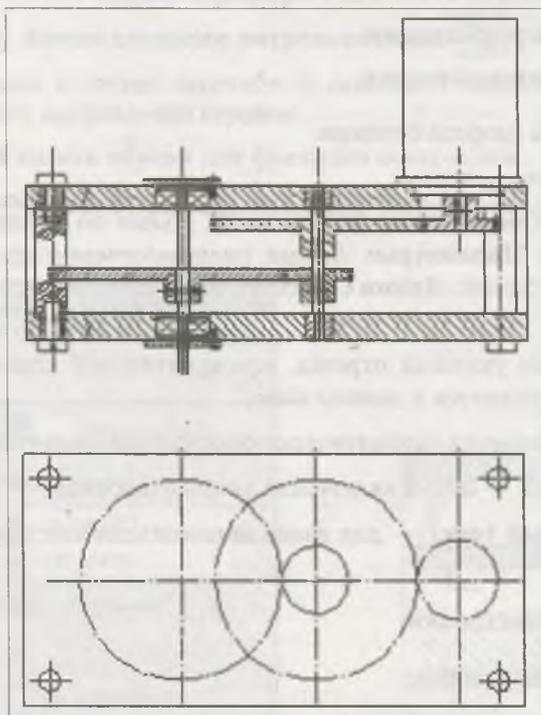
Вариант компоновки сборочного чертежа Редуктор
